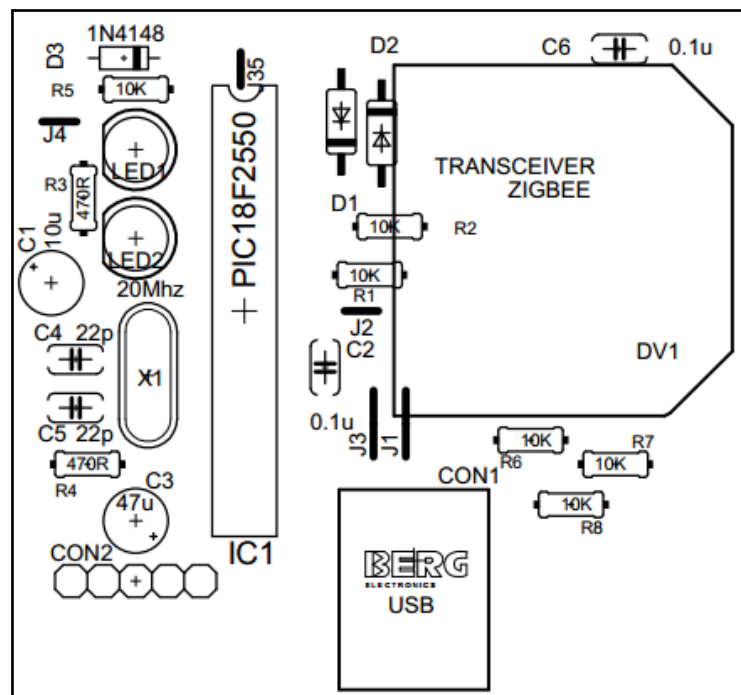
Diseño de la placa del dispositivo principal. Fuente: La Autora.
